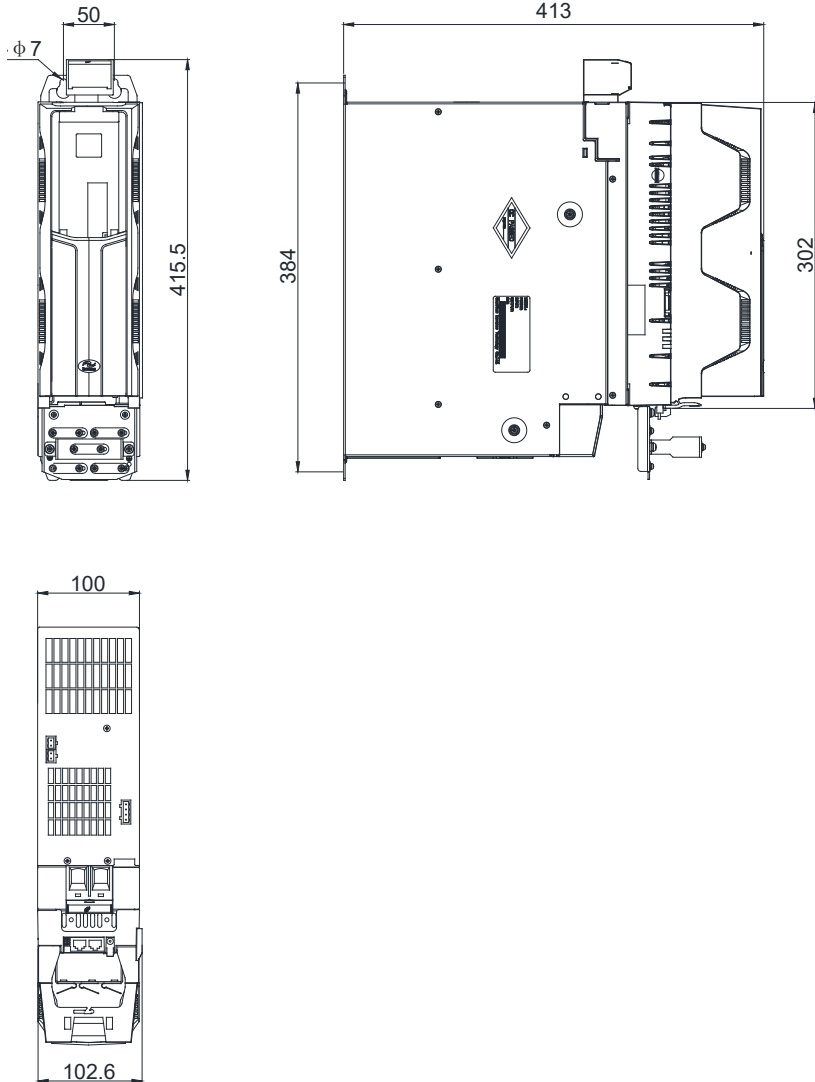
Габариты инверторов Н1...Н3 (мм)
